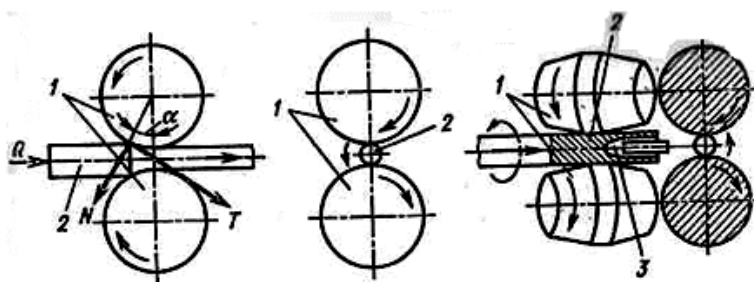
Схема поперечно-винтовой прокатки: 1-валки, 2-заготовка, 3-прошивень на неподвижной оправке.
